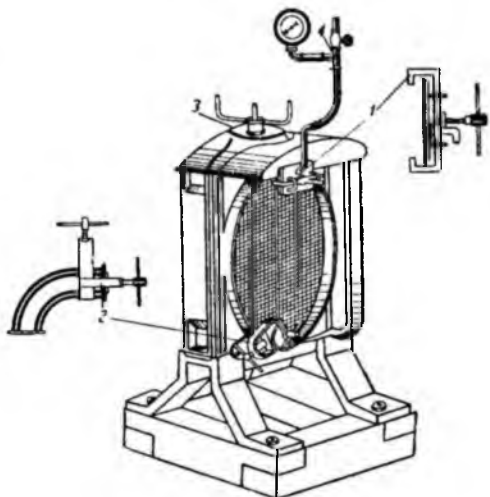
Приспособление для испытания радиаторов СХТЗ:
